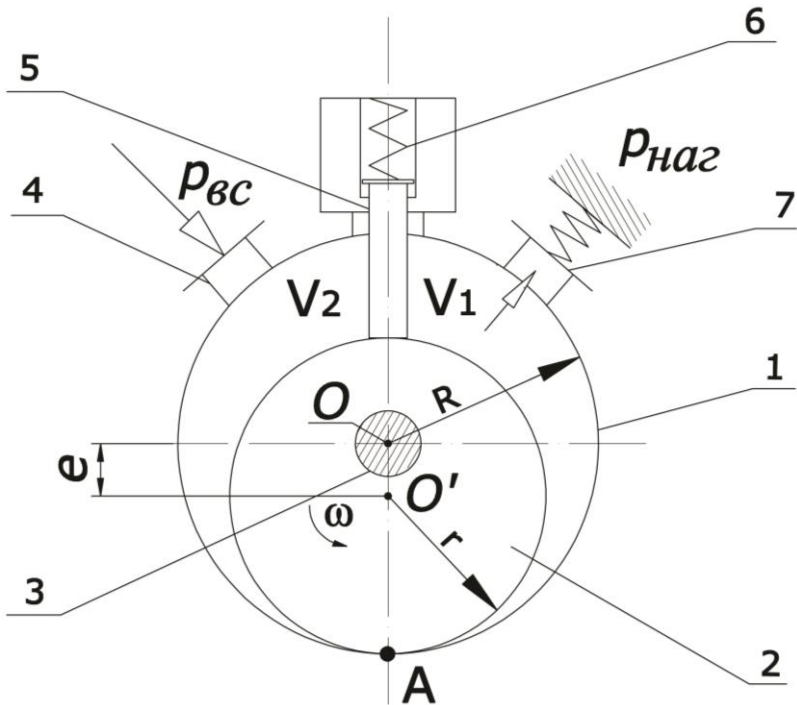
Конструкція ротаційного компресора з ротором, що котиться
